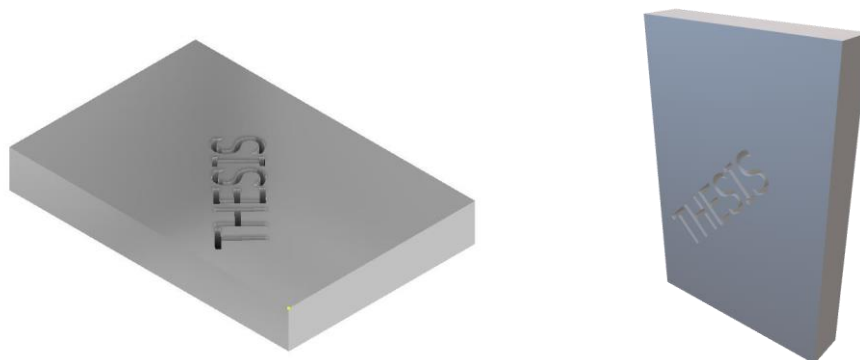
Τρισδιάστατη απεικόνιση αποστολής 31
